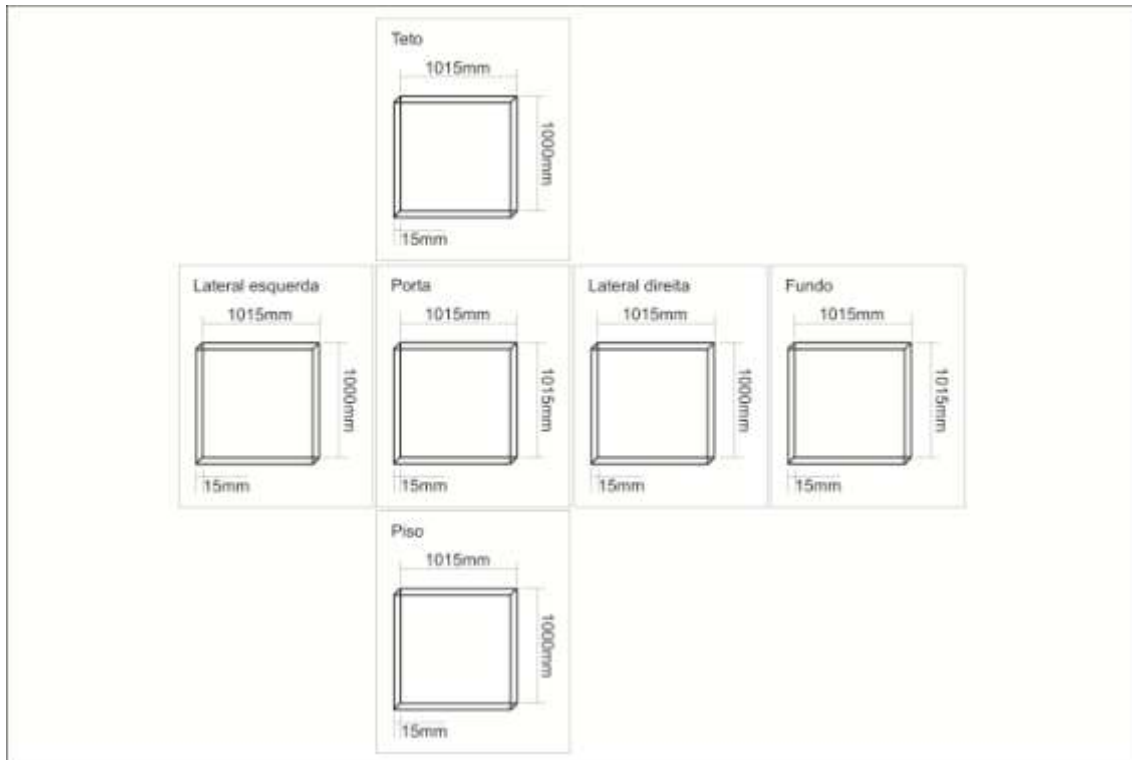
Vista plana do teto, paredes e piso do armário luminotécnico
